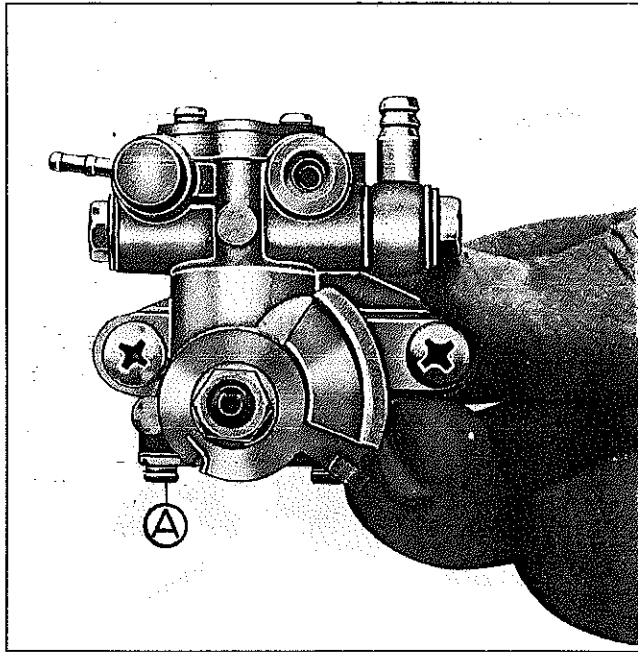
A. CONJUNTO BOMBA DO ÓLEO
